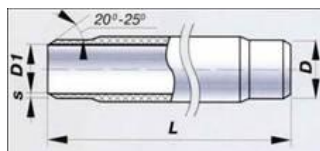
Основные размеры напорных труб (ГОСТ 539-80)
